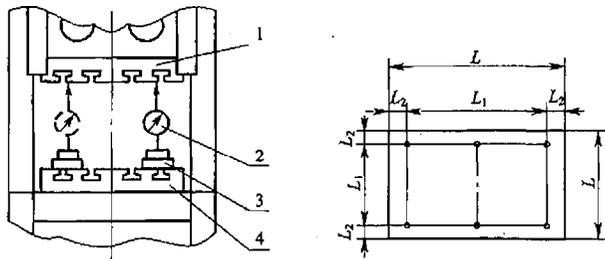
检验滑块下平面与工作台面的平行度
